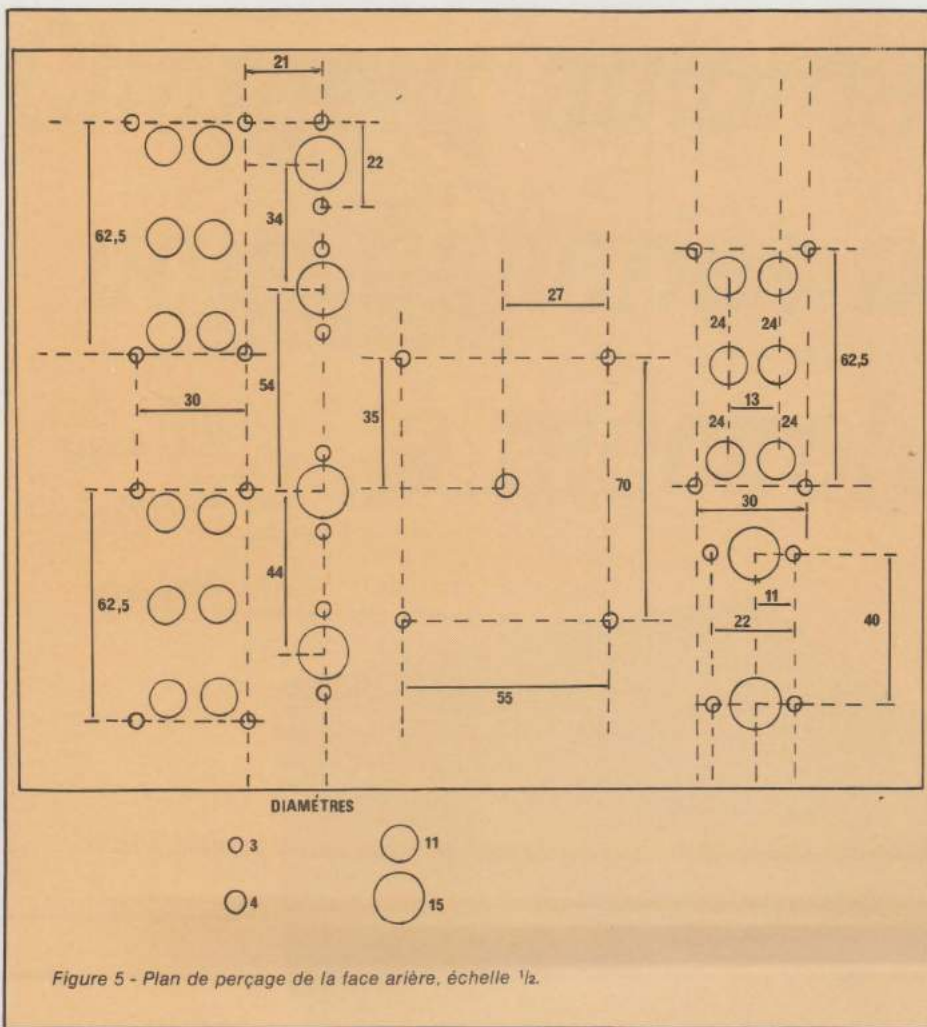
Plan de perçage de la face arrière, échelle 1/2.
